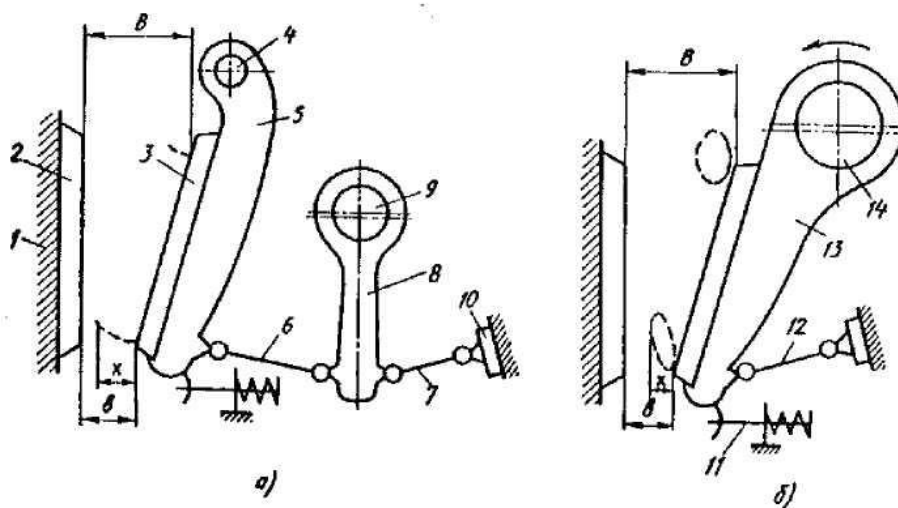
Конструктивные схемы щековых дробилок: *а* - с простым; *б* - сложным движением подвижной щеки; 1 - станина; 2 - неподвижная и 3 - подвижная дробящие плиты; 4- ось подвижной плиты; 5 - подвижная щека с простым движением; 6- передняя распорная плита; 8- шатун; 9- эксцентриковый вал шатуна; 10 - механизм регулирования размера выходной щели; 11 - устройство силового замыкания звеньев механизма подвижной щеки; 12 - распорная плита; 13 - подвижная щека со сложным движением; 14 - эксцентриковый вал подвижной щеки со сложным движением
